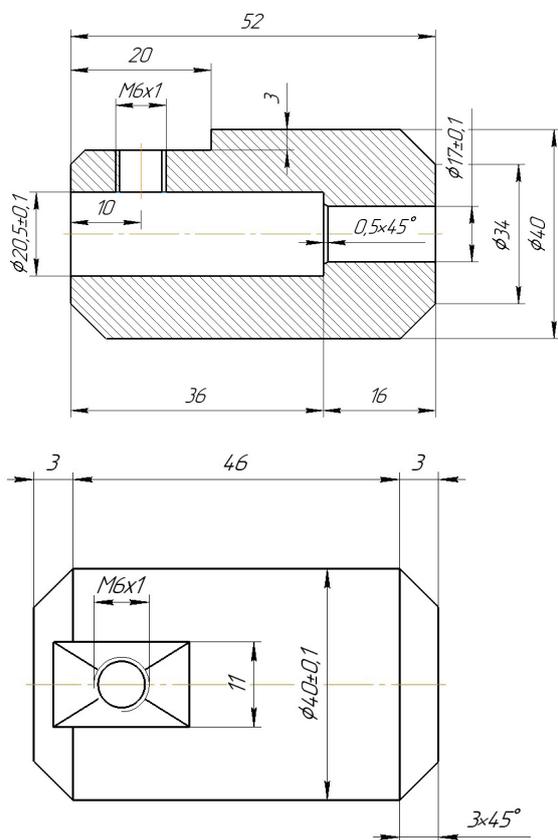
Корпус приспособления для измерения максимального хода иглы
